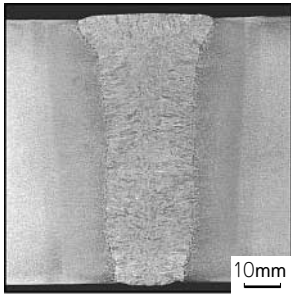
開発鋼の溶接継手のマクロ組織 (板厚 80mm)
